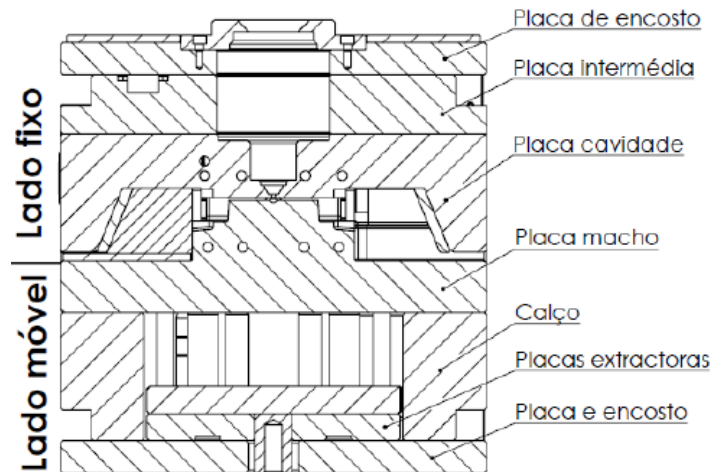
Estrutura de um molde de injeção (Harada, 2004)
